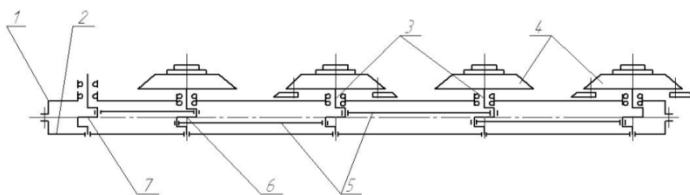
Схема режущего аппарата с приводом роторов коленчатыми валами с шатунами: 1 – основной брусок; 2 – крышка; 3 – коленчатые валы; 4 – роторы; 5 – шатуны; 6 – коленчатый вал первого ротора; 7 – приводной коленчатый вал
